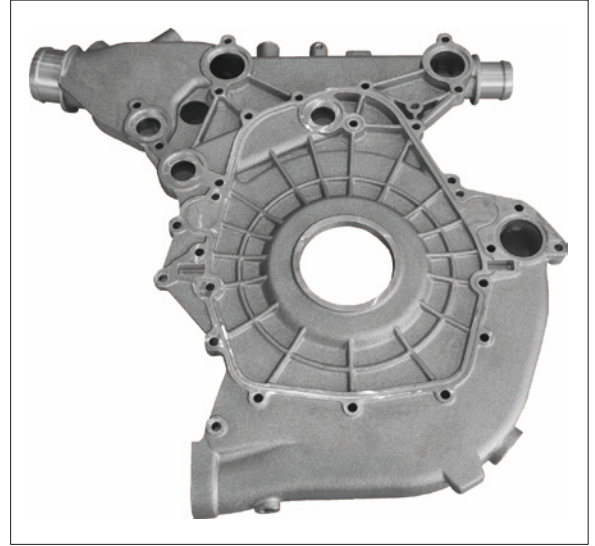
Im Aluminium-Sandguss hergestellter Motordichtflansch (Quelle: Ohm & Häner Metallwerk GmbH & Co. KG)
